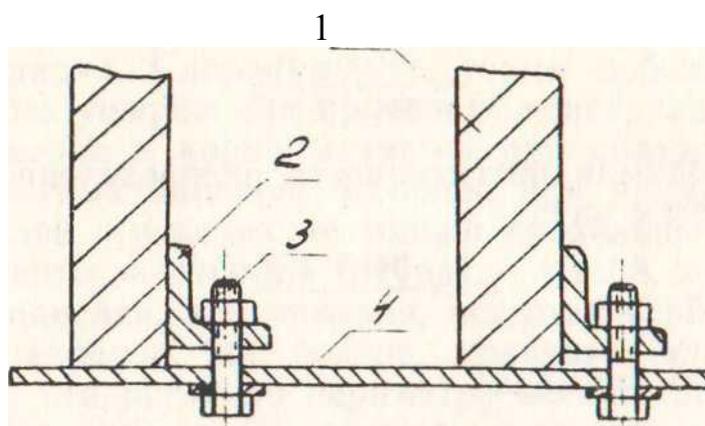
1 — рубильник; 2 — уголок; 3 — болт; 4 — обшивка.
